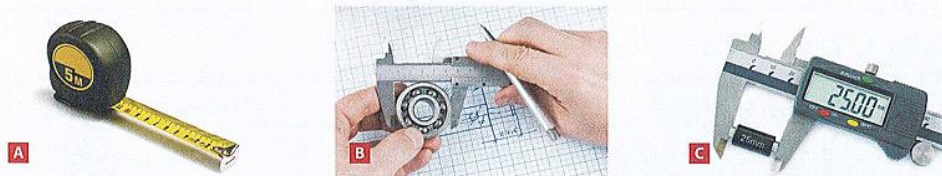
> Des instruments utilisés pour l'inspection d'une pièce
